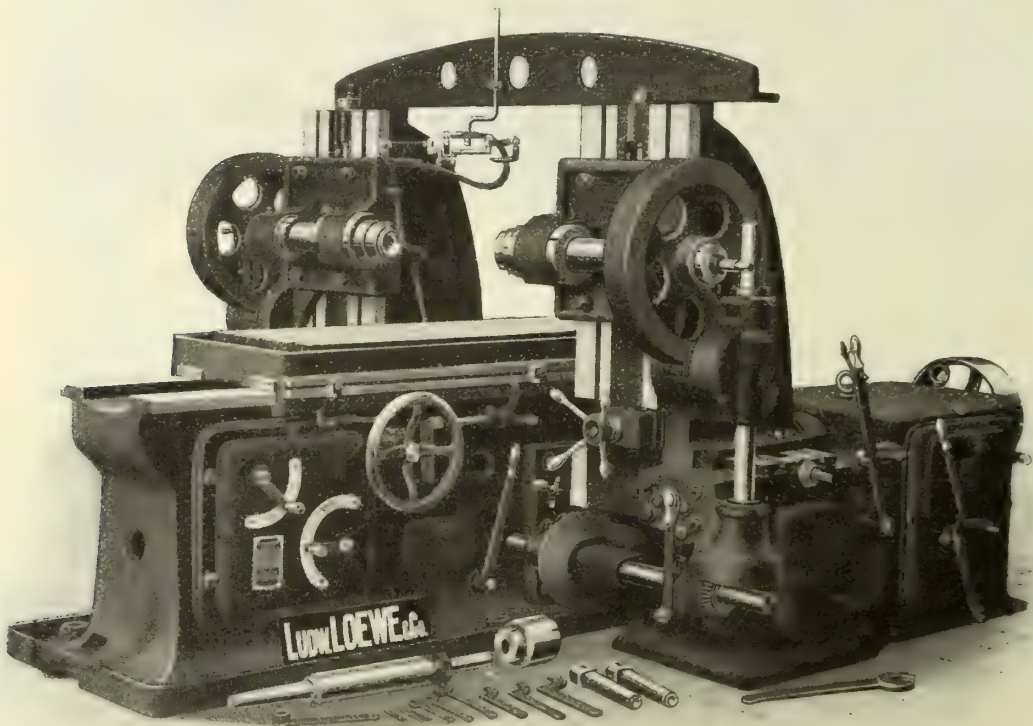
Selbsttätige Fräsmaschine mit zwei verstellbaren Arbeitsspindeln
